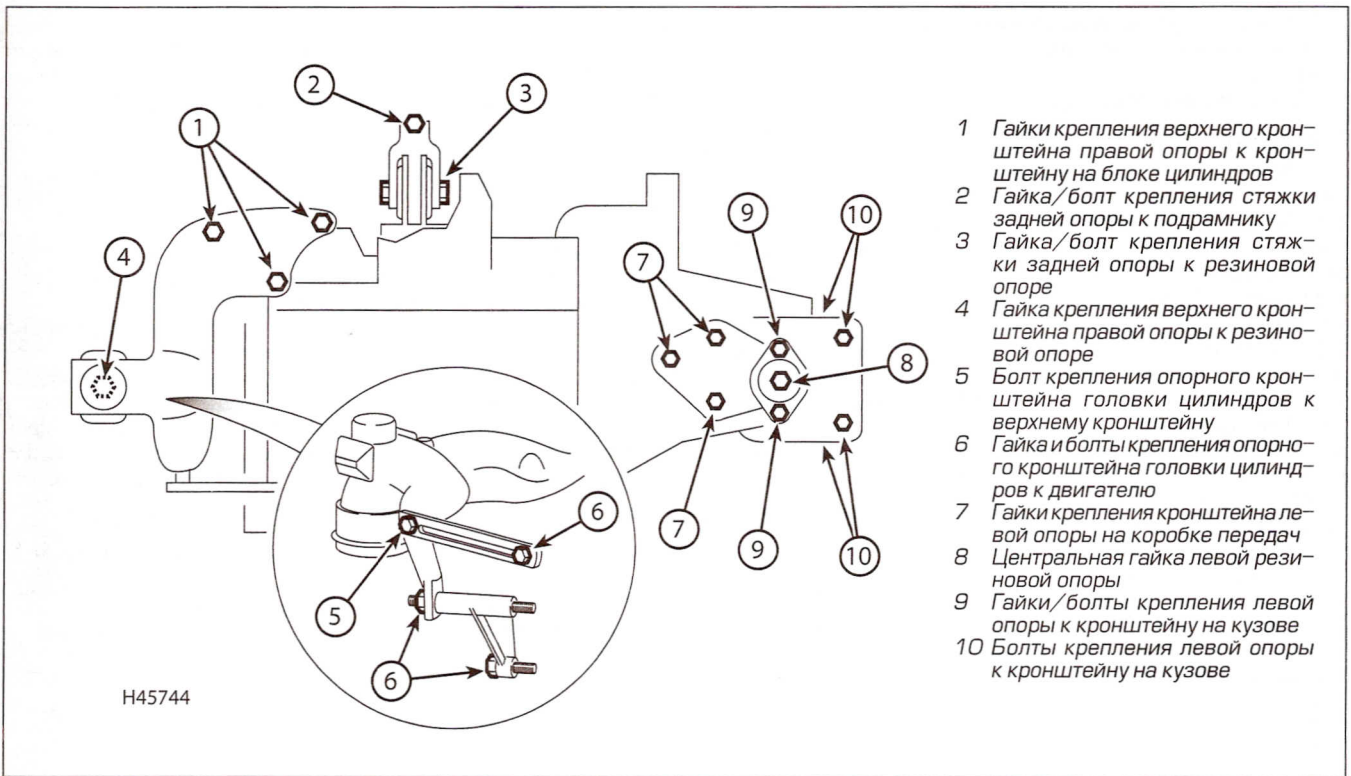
, а. Элементы и болты/гайки крепления опор двигателя/коробки передач (поздние двигатели 1.4 л)
